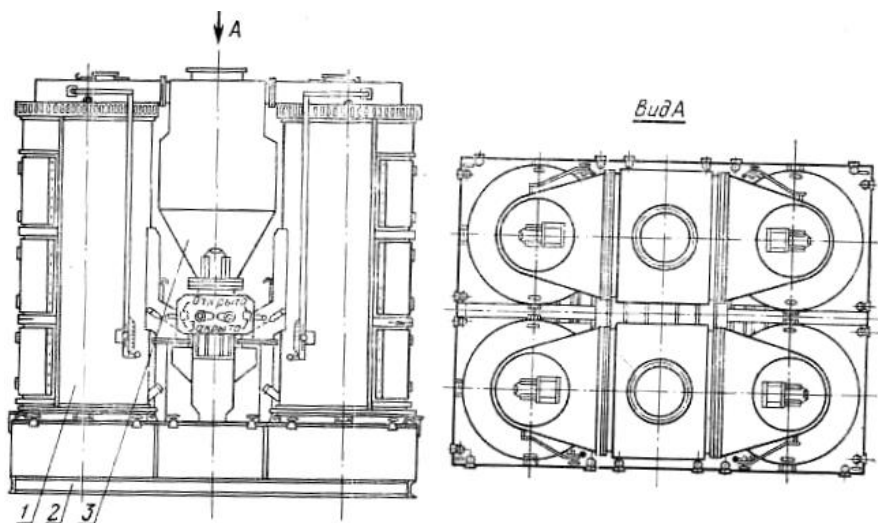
Сепаратор А1-БЦС-100: 1 - очисний блок; 2 - станина; 3 - завантажувальний пристрій
